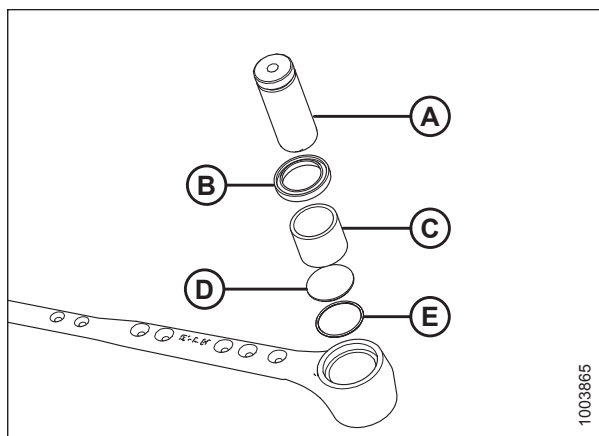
Ensamble del rodamiento de la cabeza de la cuchilla
